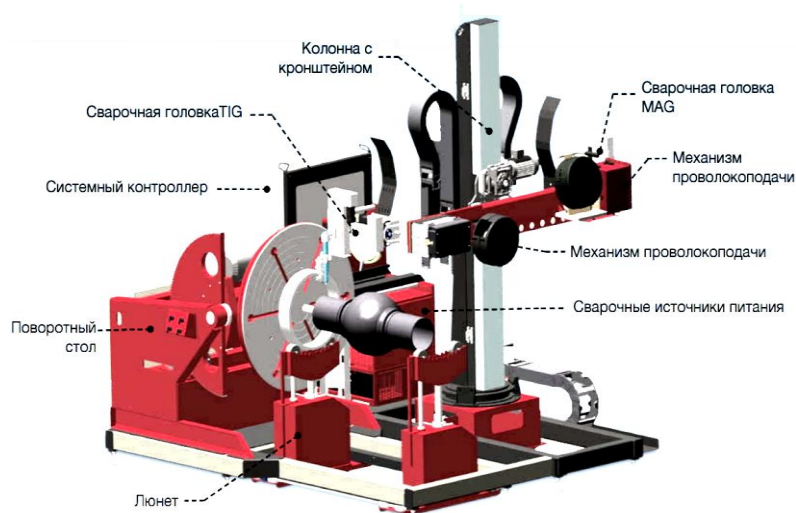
Общий вид системного компонента установки для многопроходной дуговой сварки и наплавки элементов
